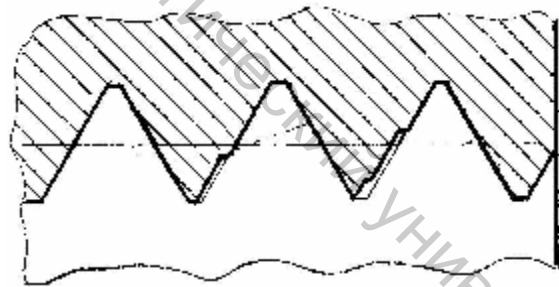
Схема подрезания боковых сторон профиля первых ниток резьбы
